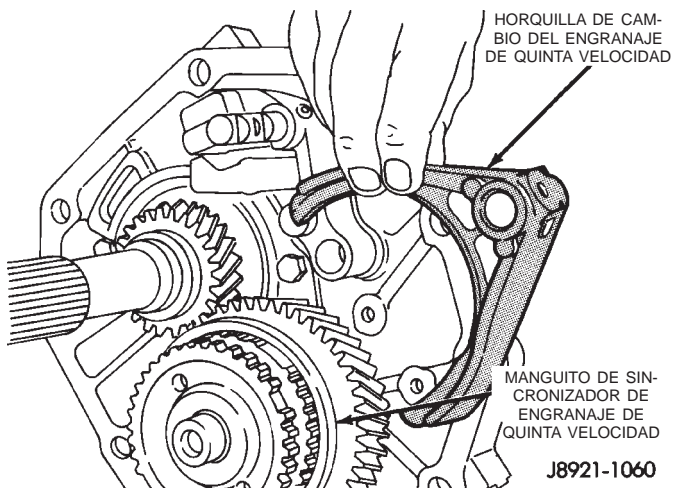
Desmontaje de horquilla de cambio de engranaje de quinta velocidad
